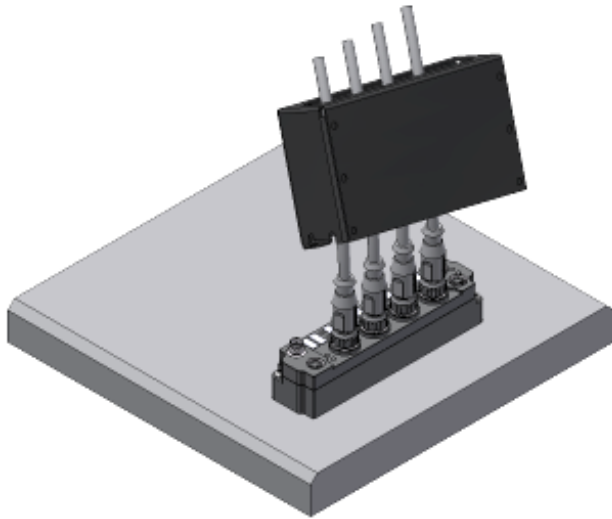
BG2000 - Anschlussleitungen festschrauben
